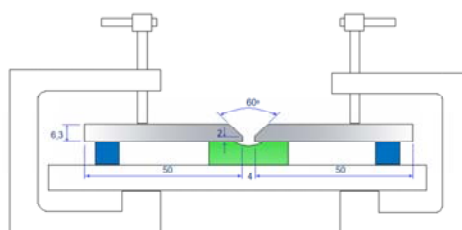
Desenho esquemático da montagem da chapa de teste para soldagem. Dimensões do chanfro, posição do suporte cerâmico, dispositivo de fixação por meio de grampos tipo “C”.
